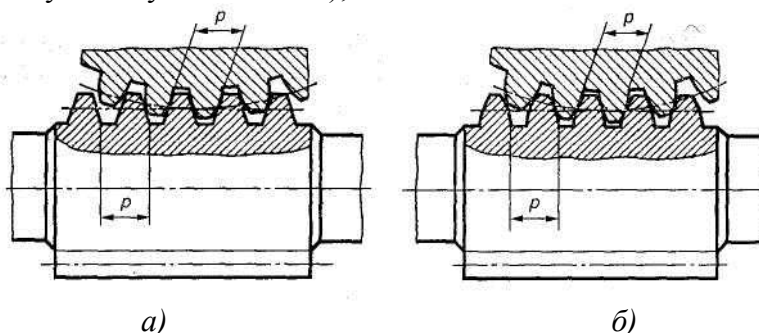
Конструкции цилиндрических червяков: а — архимедов; б — эвольвентный
